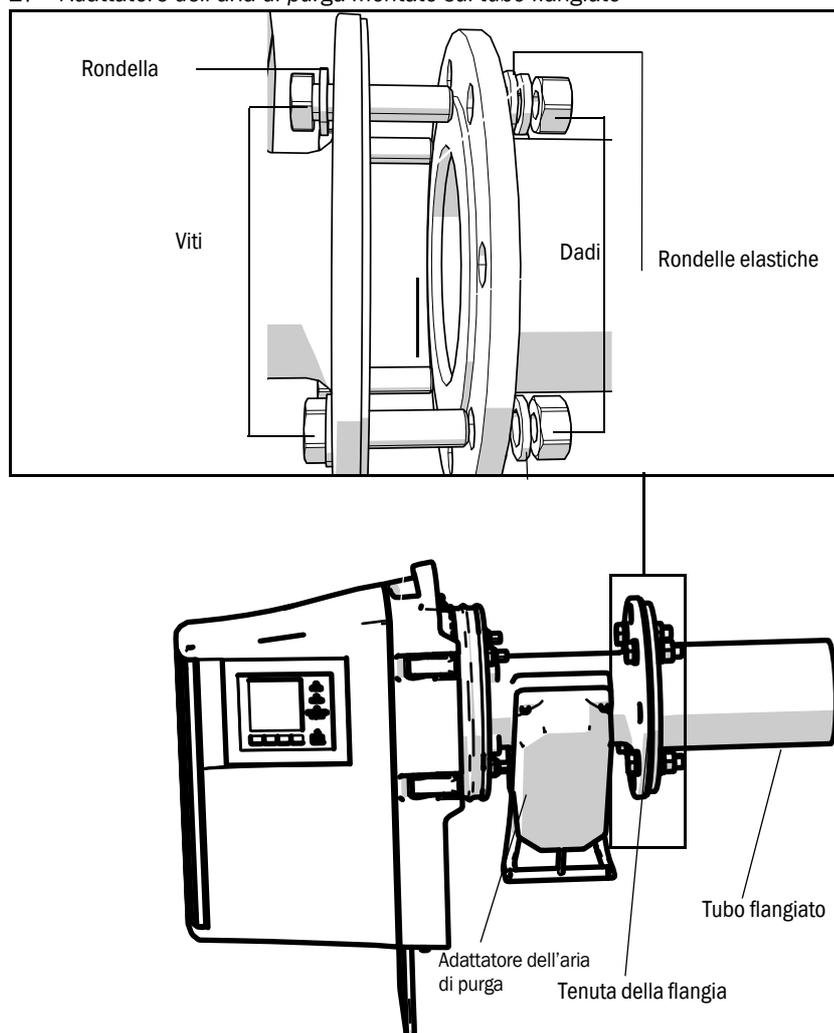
Adattatore dell'aria di purga montato sul tubo flangiato
